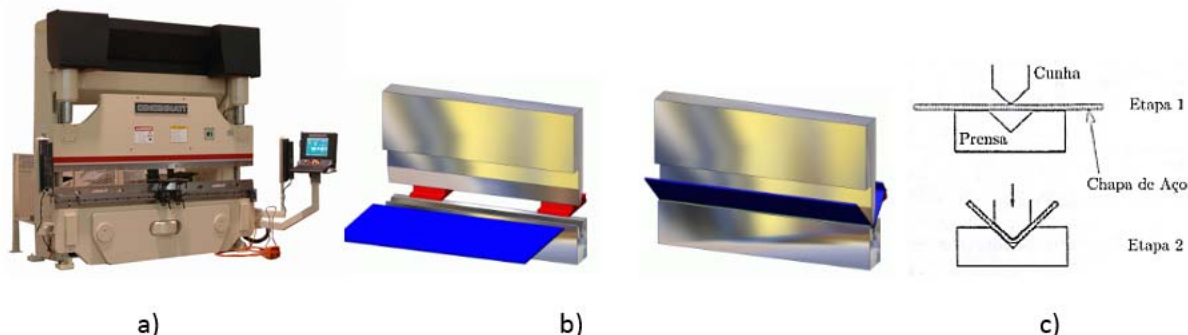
a) Quinadora; b) Processo de quinagem (FUTURENG@); c) Etapas de quinagem (Veríssimo, 2008).
